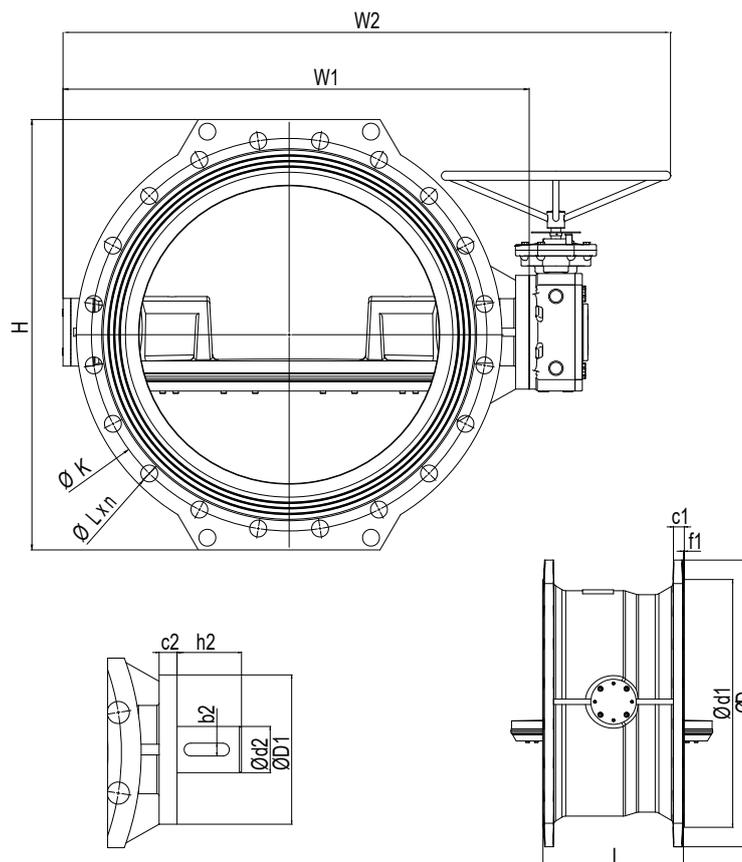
Disegno di sezione PN 16 DN 100 - 800
